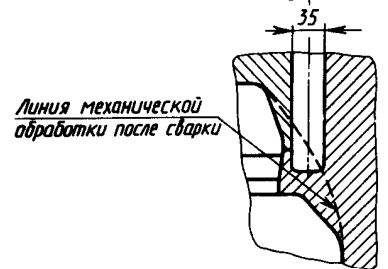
Конструкция соединения сферической крышки с фланцем корпуса реактора
